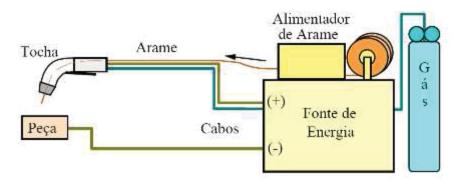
Equipamento de solda com arame tubular Bernados (Fonte: adaptada do catalogo ESAB)
